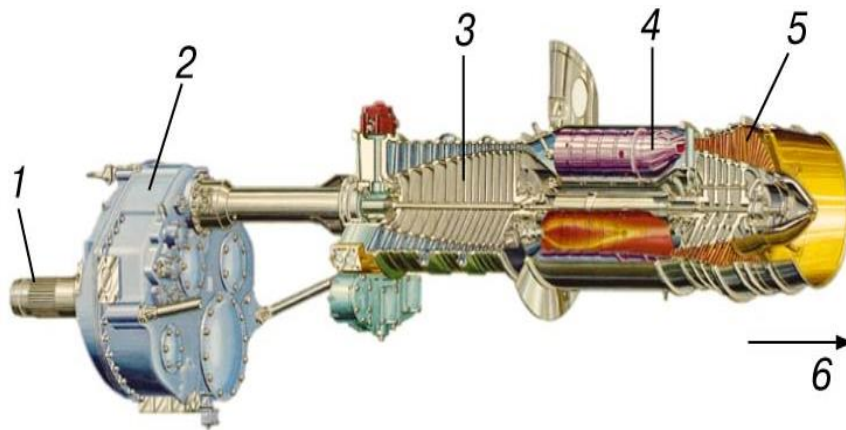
Турбовинтовой двигатель: 1 – вал винта; 2 – редуктор; 3 – компрессор; 4 – камера сгорания; 5 – турбина; 6 – сопло.
